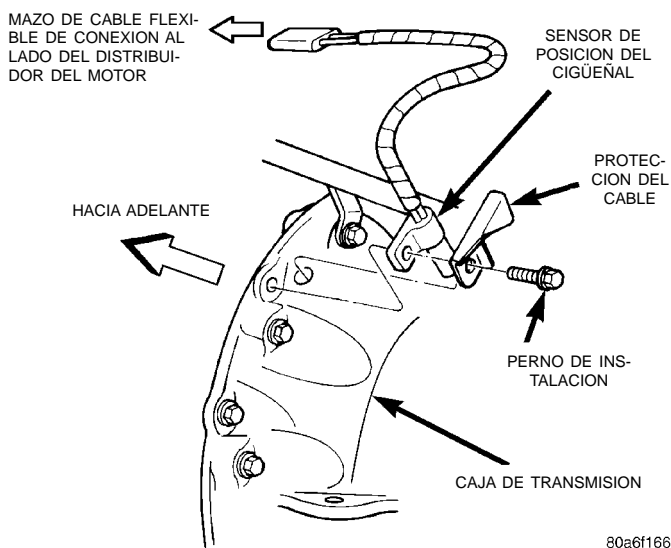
Sensor de posición del cigüeñal—Motor de 4.0L
